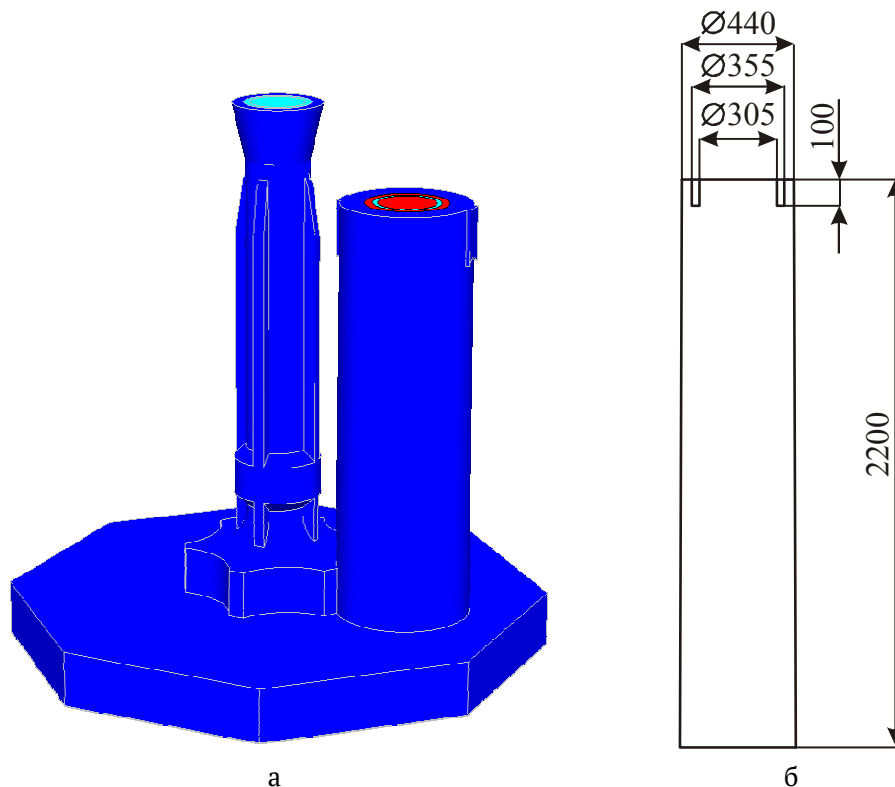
Загальний вигляд ливарної форми (а) і схема розміщення корпусного холодильника в злитку з надливною вставкою (б)
